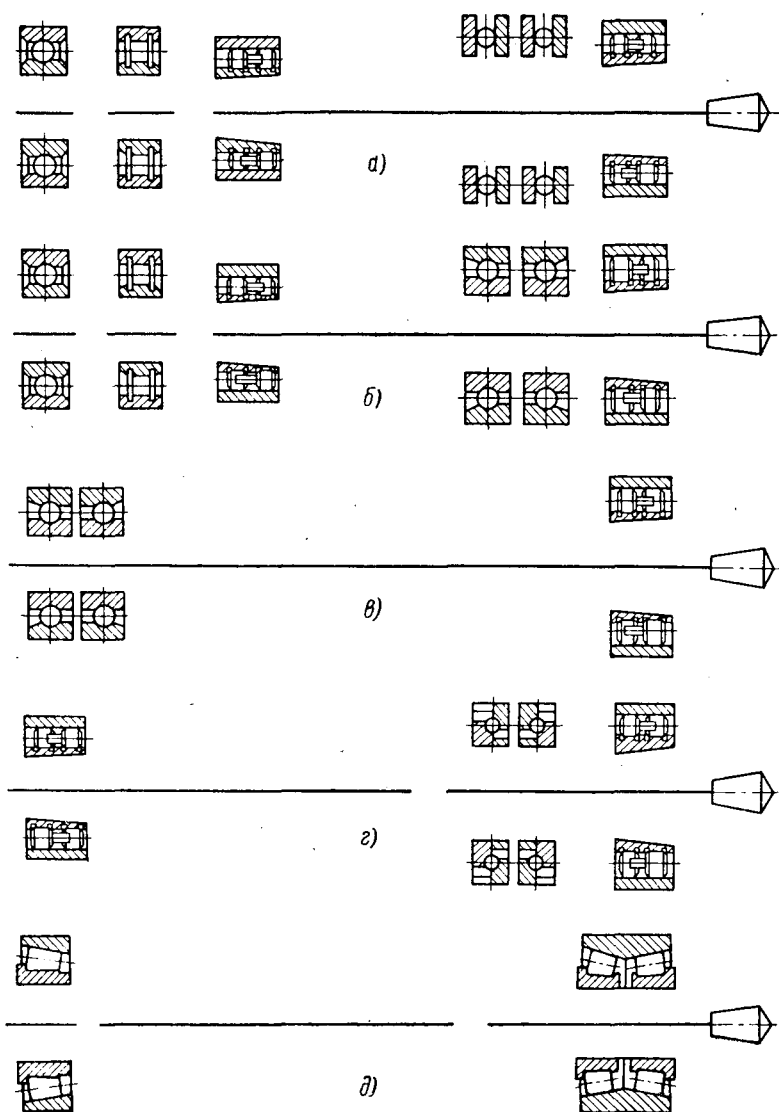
Схемы компоновки подшипников качения для шпинделя:
